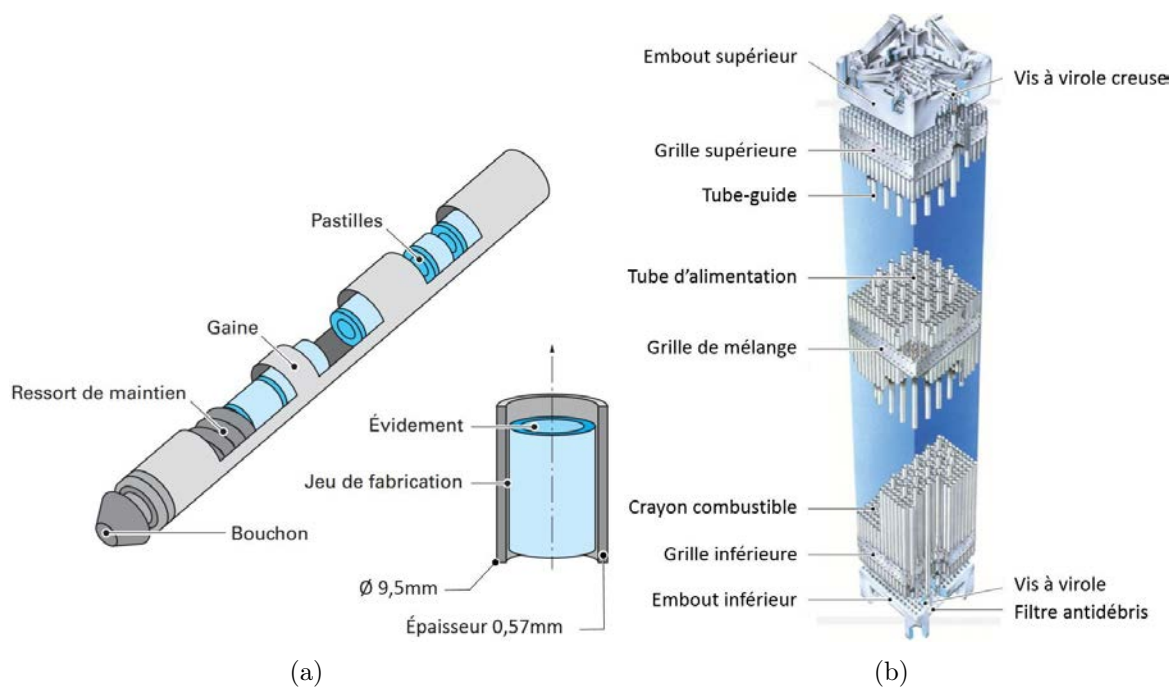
(a) Vue éclatée d'un crayon combustible ; (b) Schéma d'un assemblage combustible [7].
